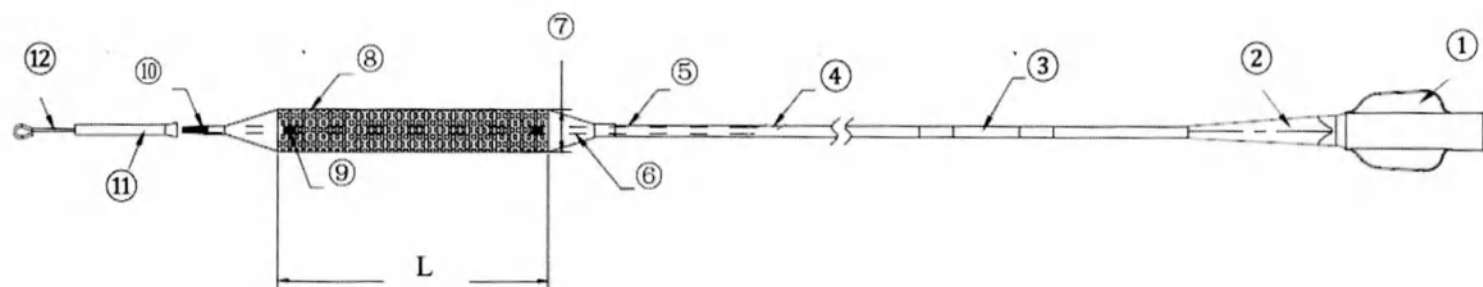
Схематичный чертеж изделия/ Fig.11-3 Product structure diagram
